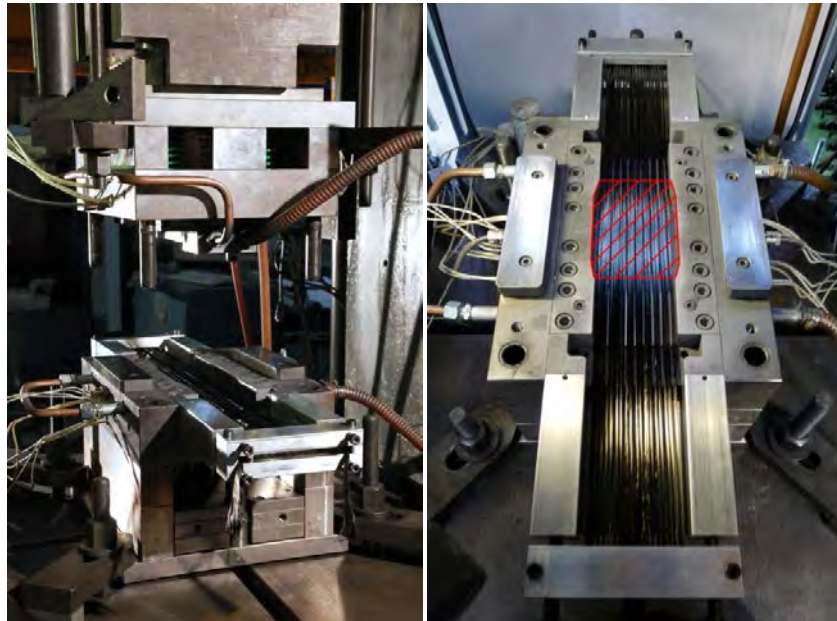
Vorspannvorrichtung im eingebauten Zustand; *links*: vollständige Darstellung des Werkzeugs; *rechts*: Draufsicht des unteren Teils des Werkzeugs
